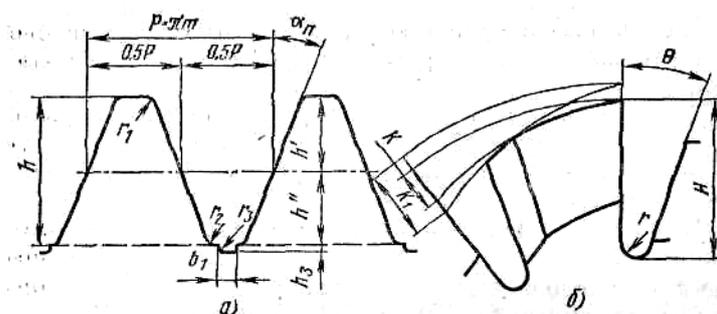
Схемы для определения элементов профиля (а) и затылования зубьев (б) червячной фрезы.
